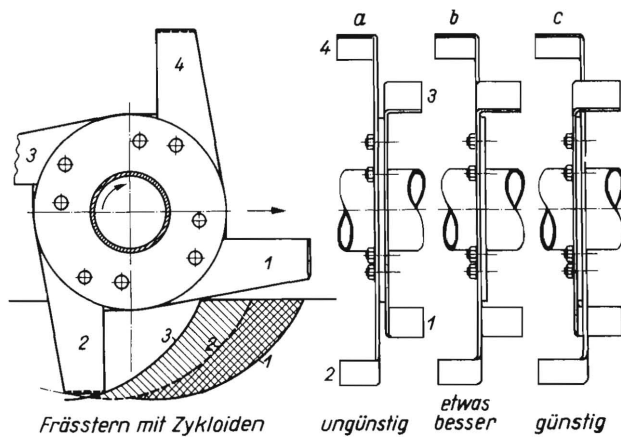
Verschiedene Anordnung der Werkzeughalterung auf einem Kranz unter Berücksichtigung des Schnittwiderstandes am Werkzeugstiel.
